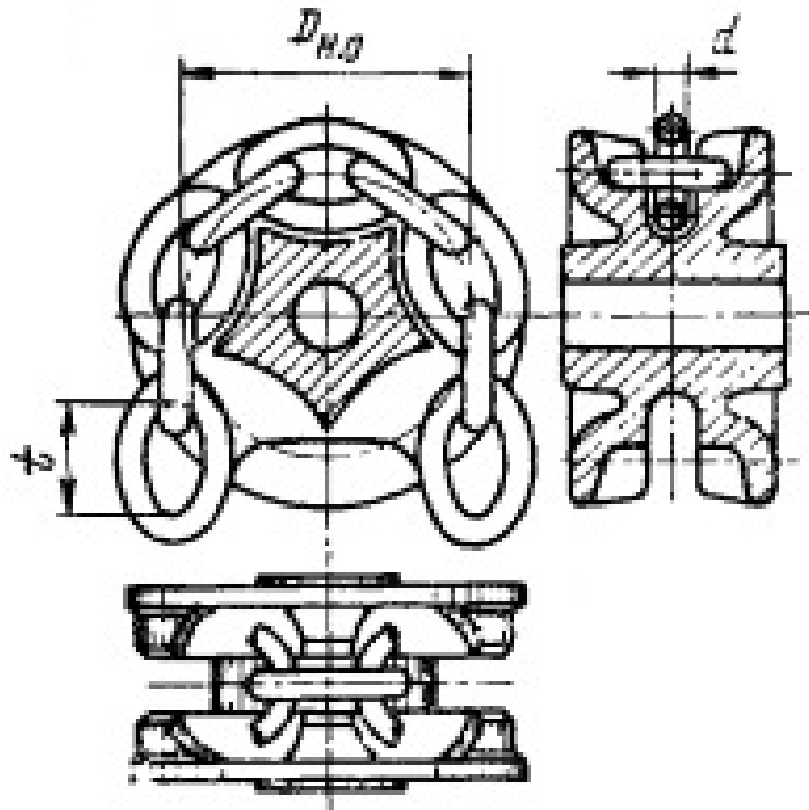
Приводная звёздочка механизма передвижения тележки
